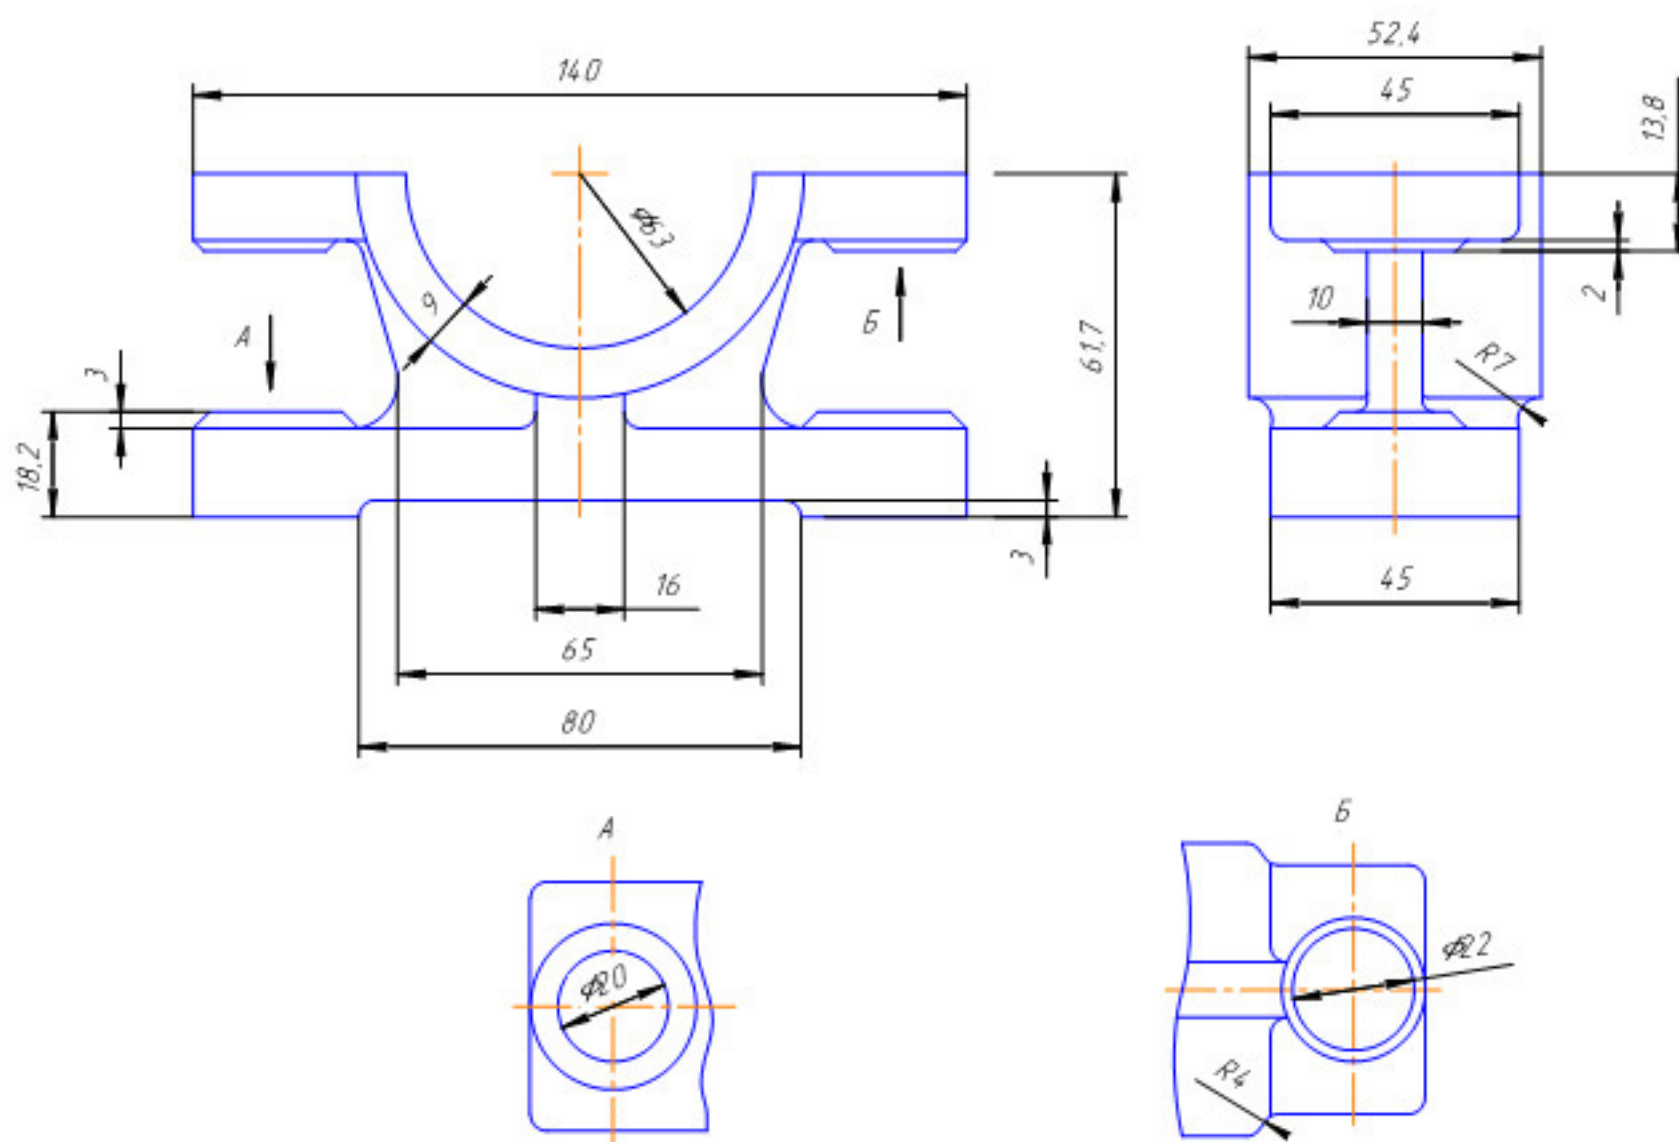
Ескіз заготовки, виготовленої литтям за виплавними моделями
